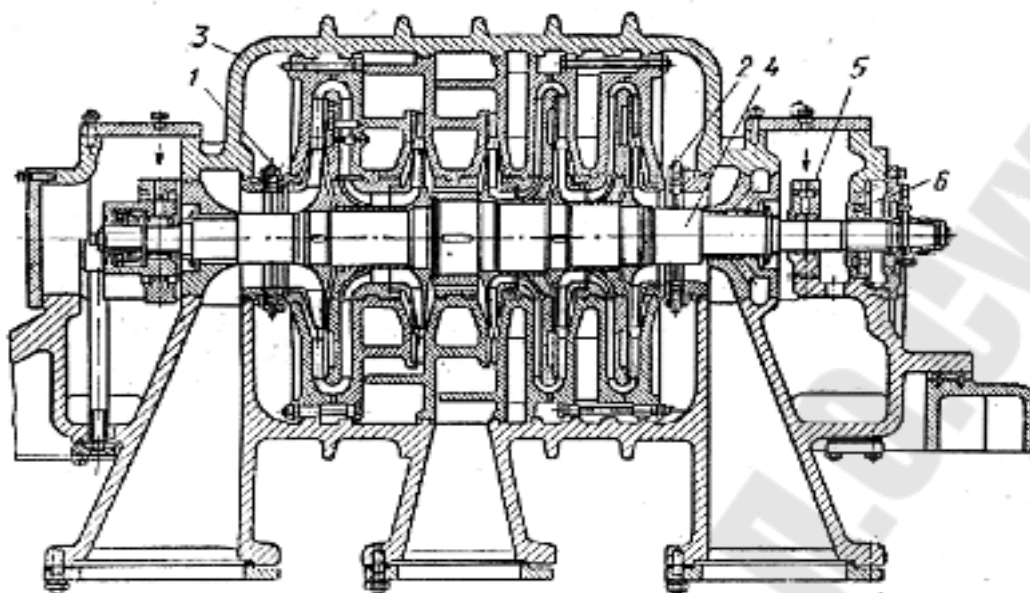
[13]. Аммиачный центробежный компрессор ТКА-545:
